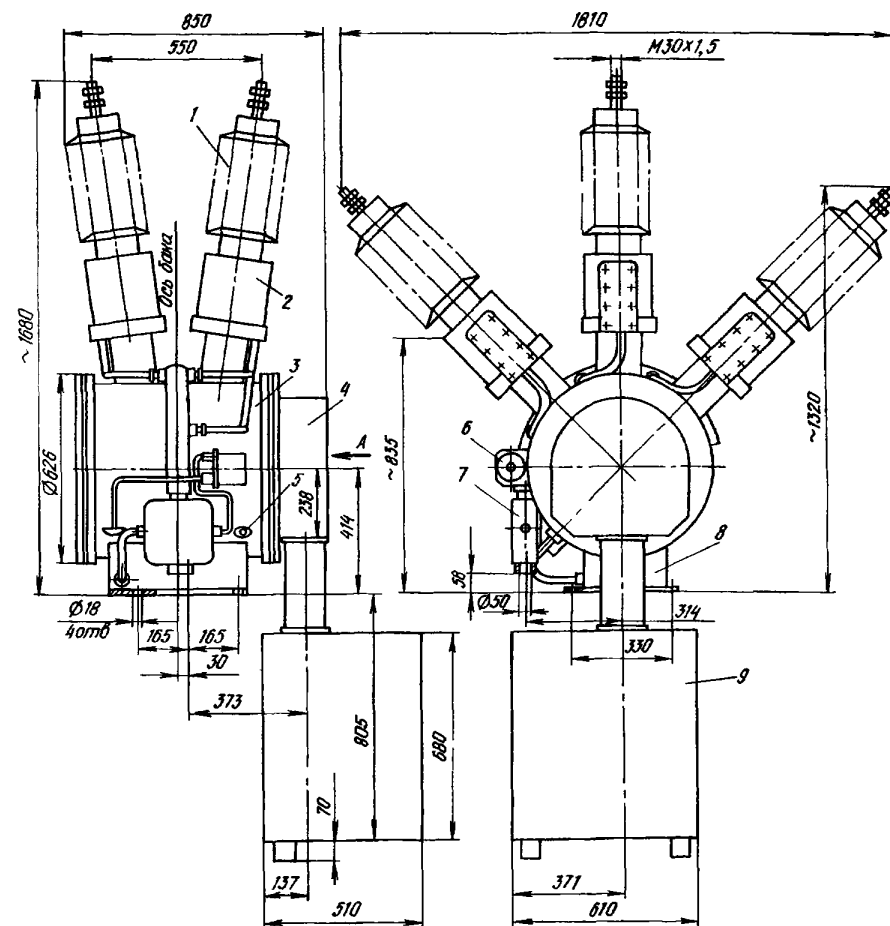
Габаритные, установочные, присоединительные размеры выключателя типа ВГБЭ-35
